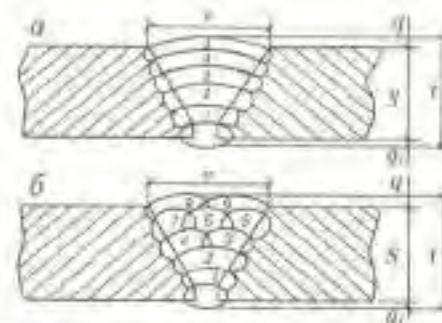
Зварювання багатшарових і багатпрохідних швів із зворотнім підварюванням кореня:
